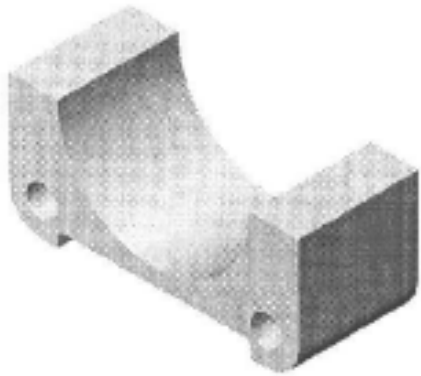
Вигляд деталі у PhotoView 360
